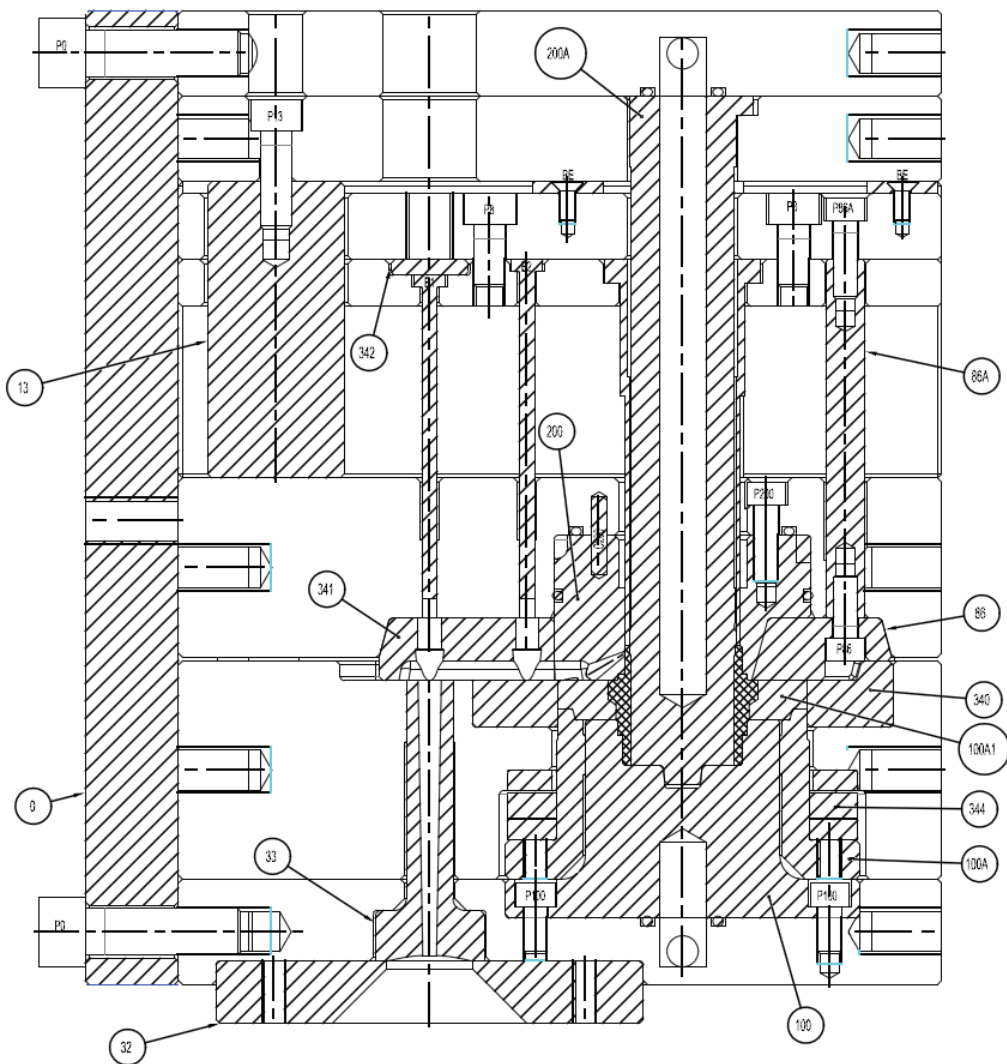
Molde de injeção com indicação dos vários componentes do molde 827 (vista em corte: seção A-A (desenho 2D final para montagem)).
